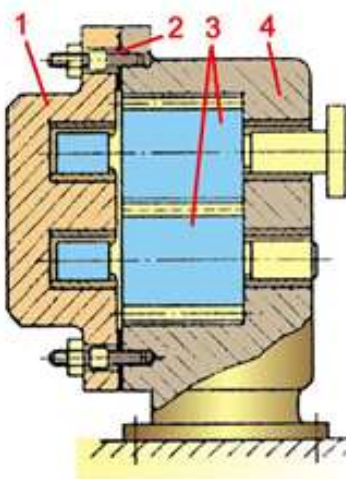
Шестерёнчатый смазочный насос [9]
